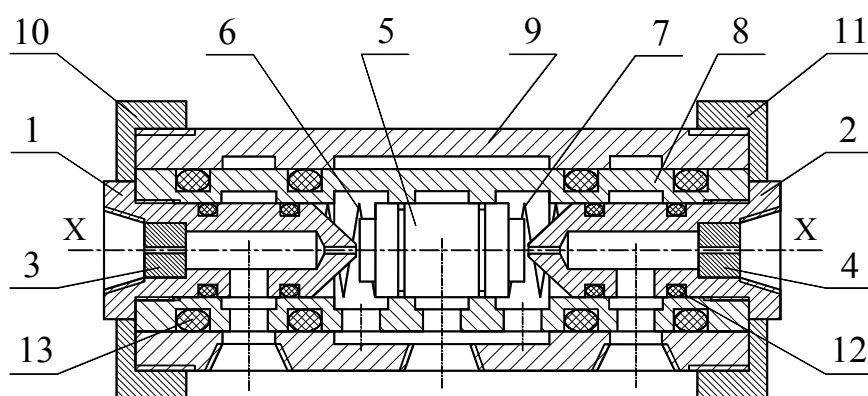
Конструкция измерительного преобразователя ускорений типа сопло – заслонка
